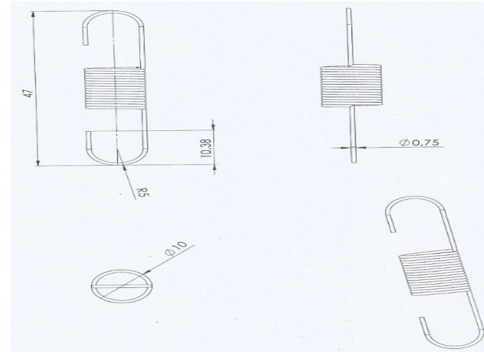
Alternatif kilit modeli teknik ölçüleri
